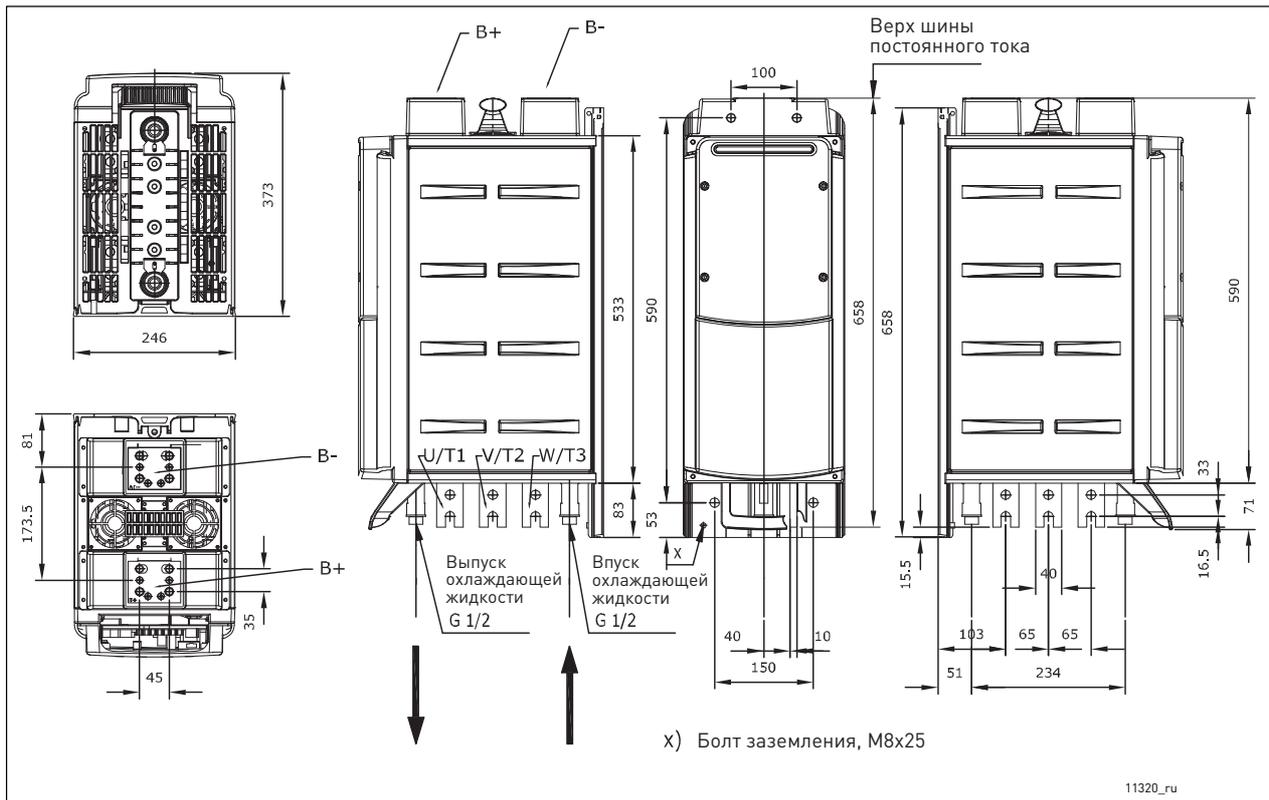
Инвертор VACON® Liquid-Cooled, CH61
